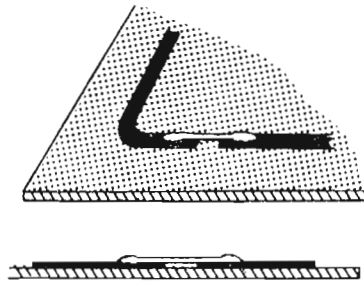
Riparazione della rottura di un collegamento stampato, mediante saldatura di un segmento di conduttore sovrapposto longitudinalmente, nel punto di interruzione.
